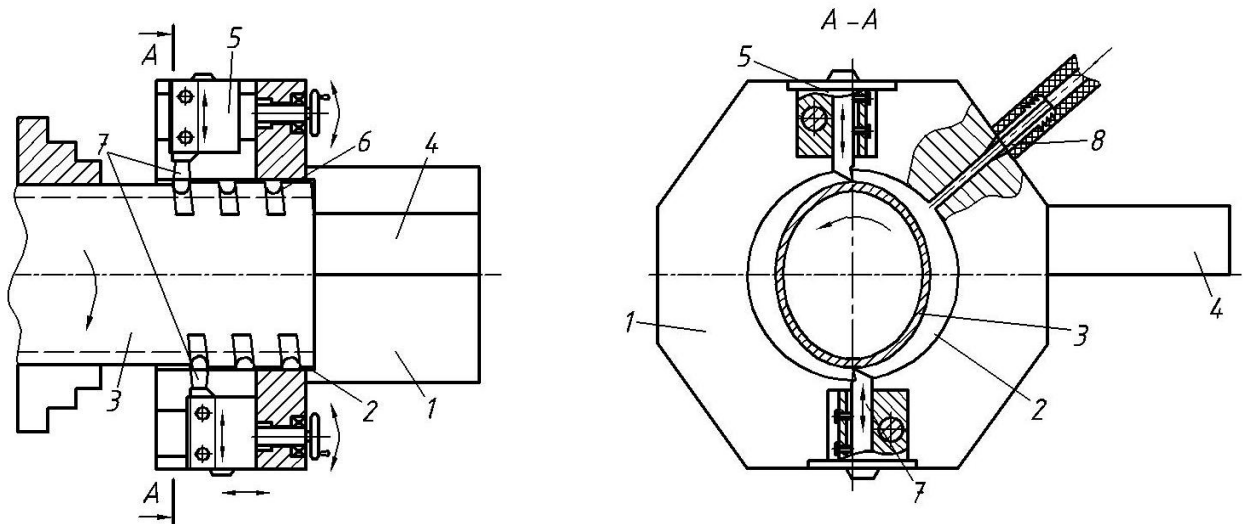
Схема пристрою для нарізання зовнішніх профільних гвинтових канавок: 1 – корпус; 2 – наскрізний отвір; 3 – еліпсна оправа; 4 – державка; 5 – різцетримач; 6 – гвинтова канавка; 7 – різальні інструменти; 8 – штуцер для підводу МОР
